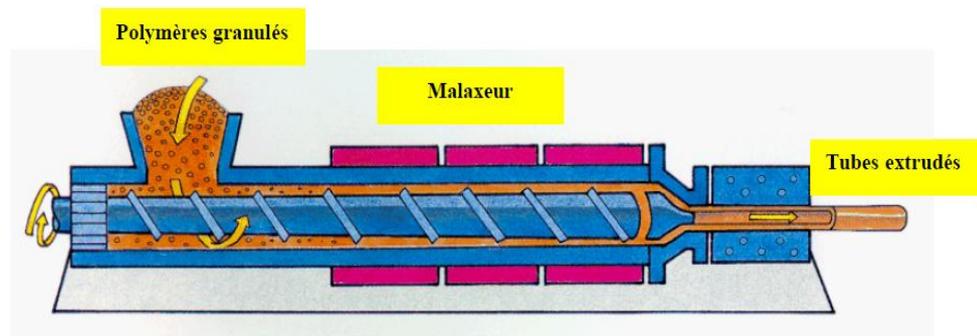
Représentation d'une machine d'extrusion des tubes.
